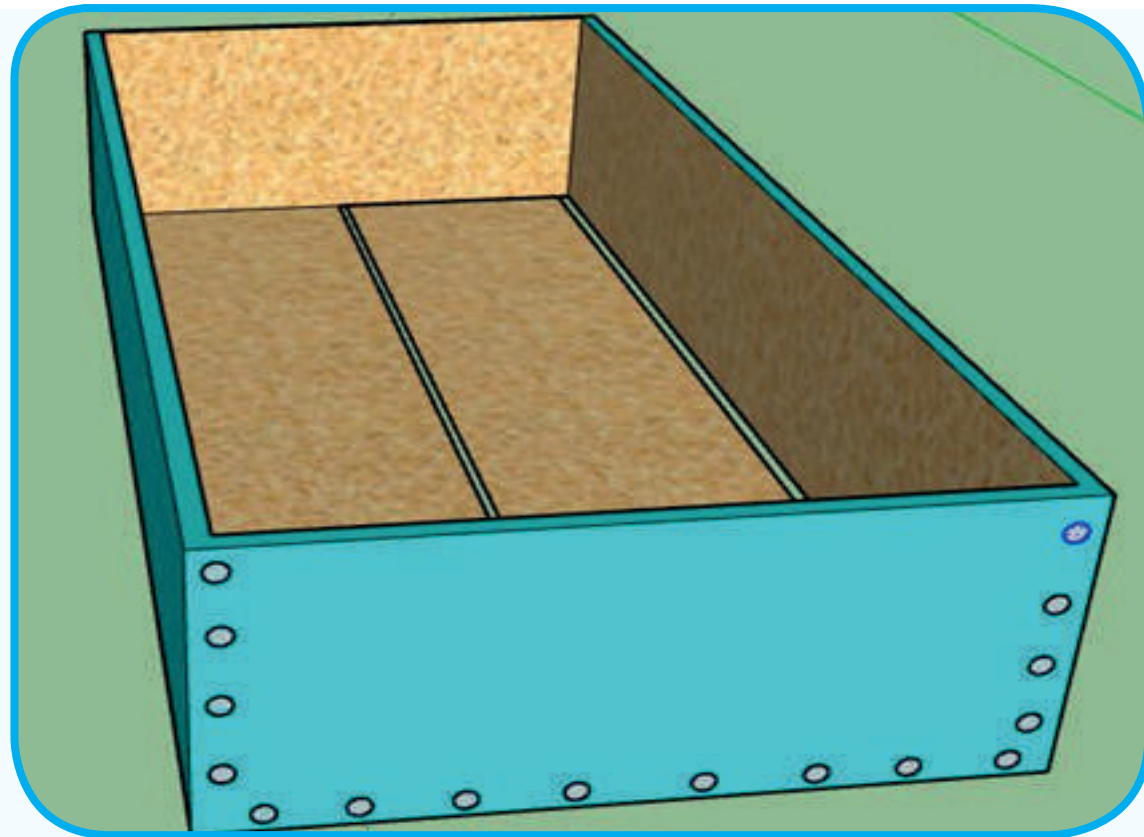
Tablas de fondo para la cama elevada. (Autora, 2018)
